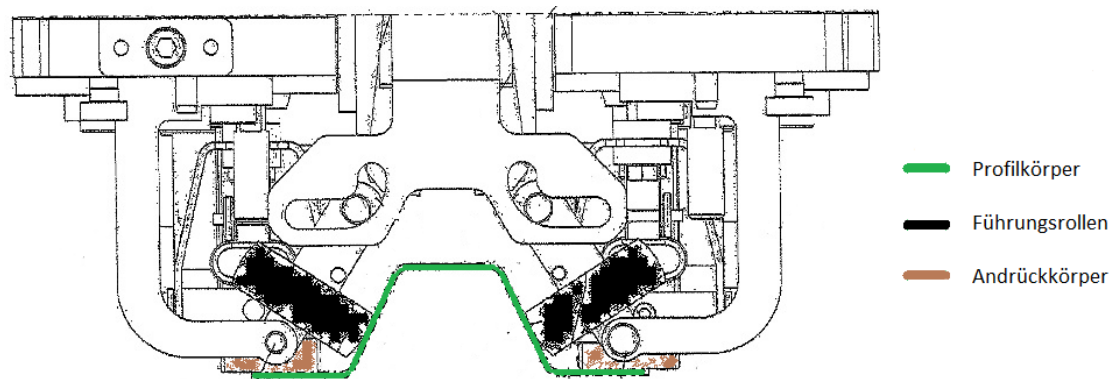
Aufnahme Werkzeug nach FFT EDAG [26]
